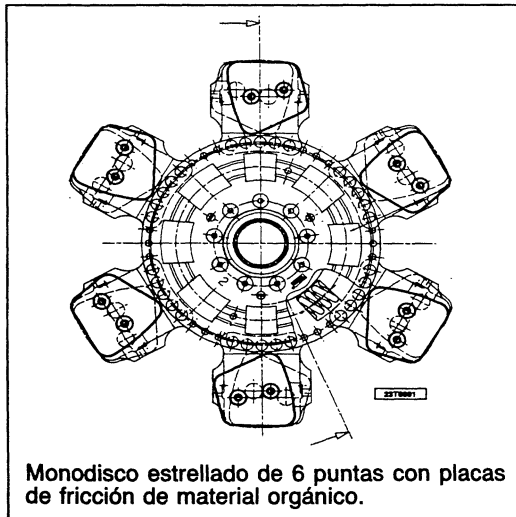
Disco embrague para Explorer 90 "DUAL TRAC SYSTEM".
